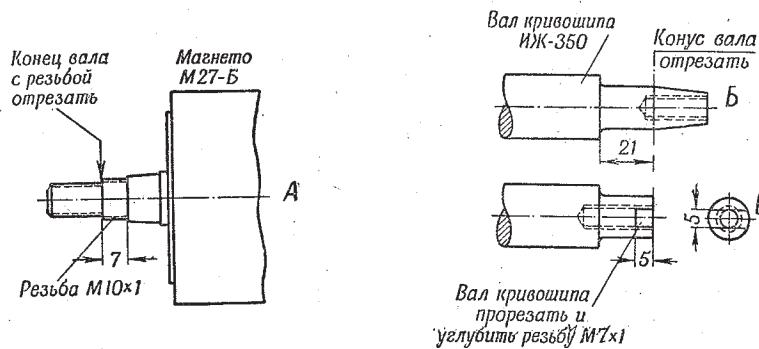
Укороченный вал кривошипа и деталь вала магнето:
